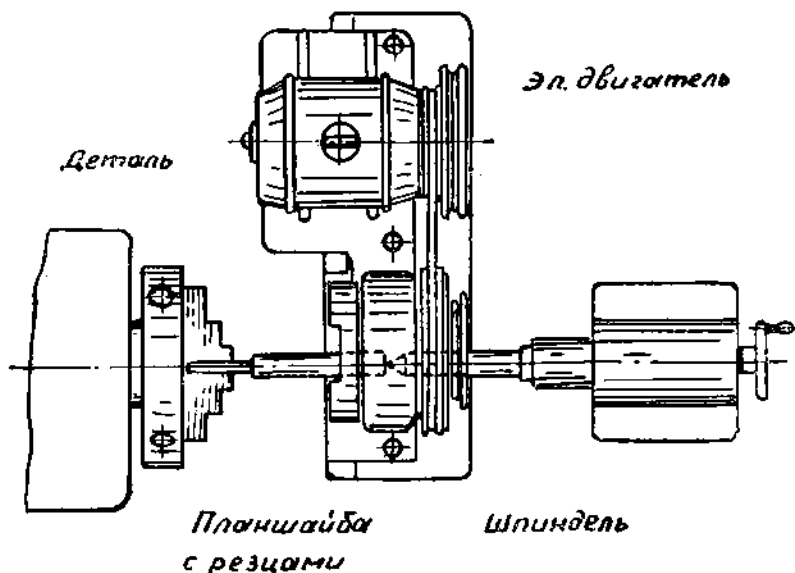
а. Скоростная нарезка вращающимися резцами
